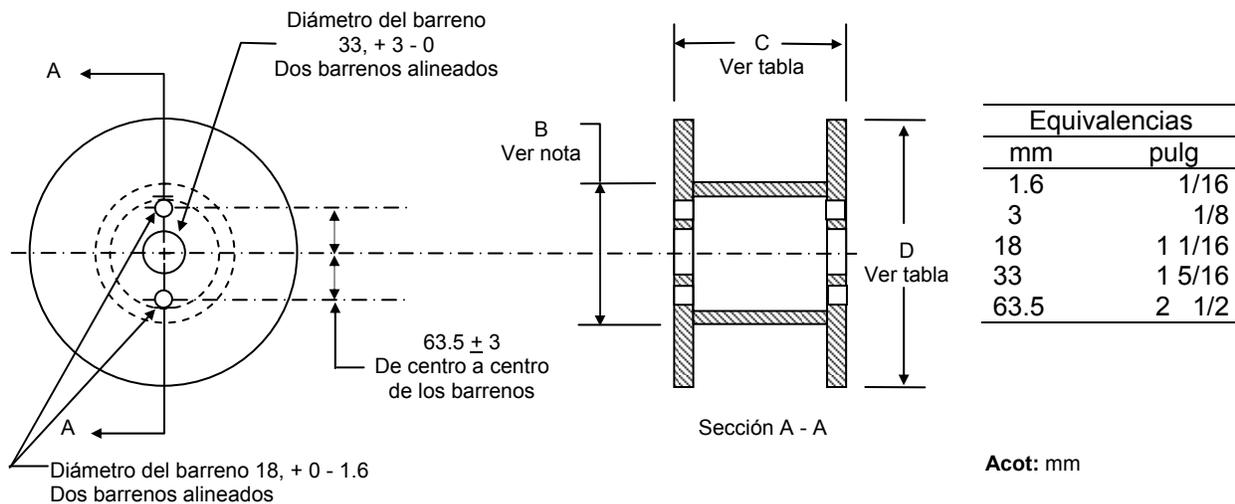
(A). CARRETE – DIMENSIONES DEL CARRETE DE 102 mm (4 PULGADAS).
